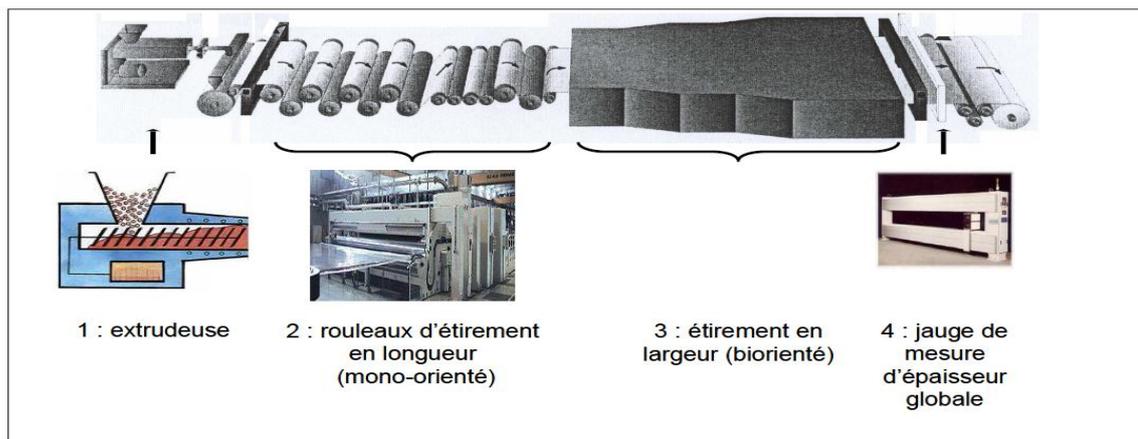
ligne de fabrication par extrusion à plat. [48].
